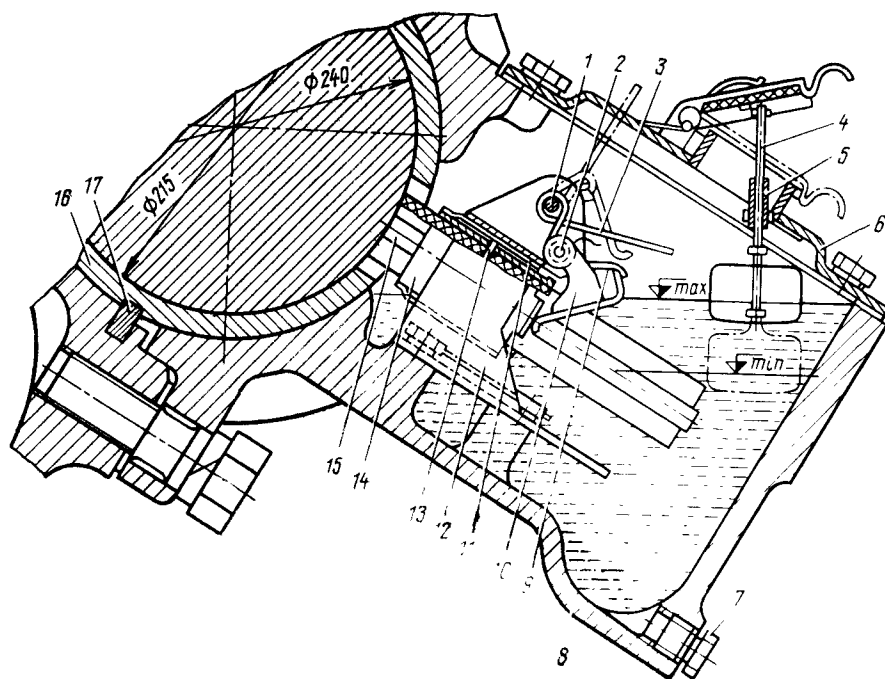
Моторно-осевой подшипник с polyesterной системой смазки:
